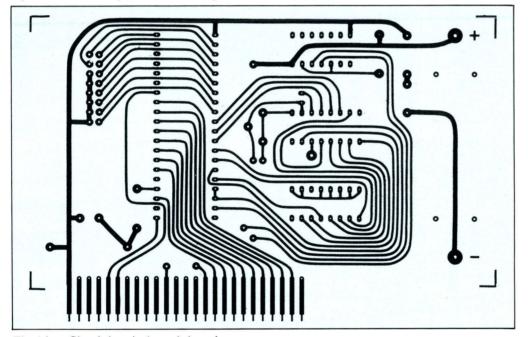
b. - Circuit imprimé vu côté soudures.
